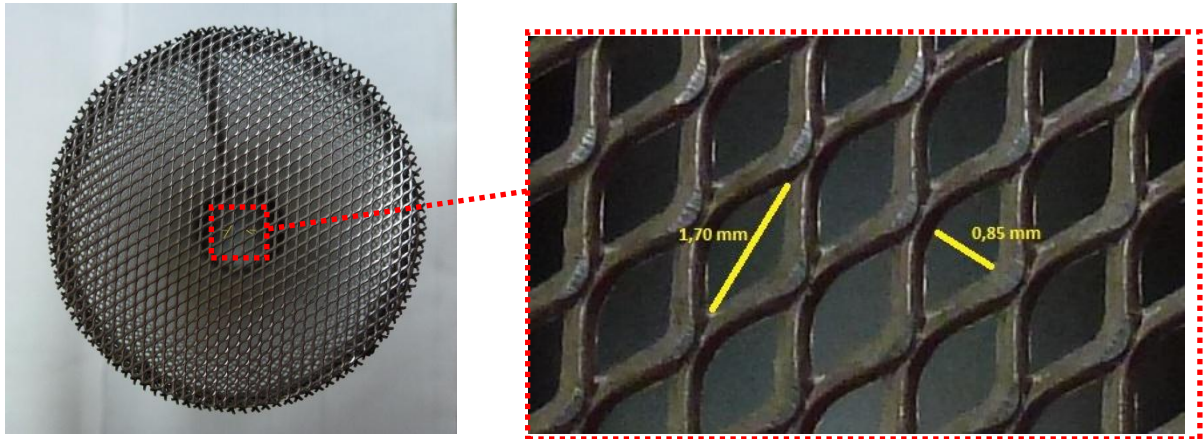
dimensioni fori schermo del bocchettone carburante AS350 B3.
